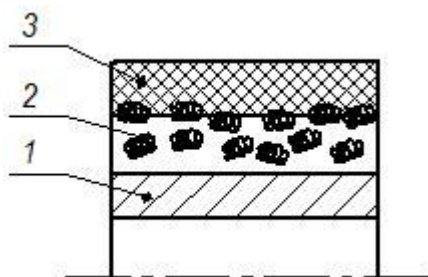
Фторопластовый подшипник с эластичной подложкой из материала МР
